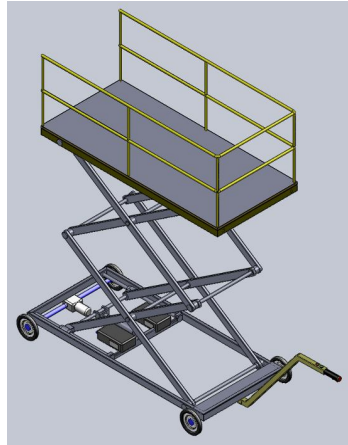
Vista isométrica do projeto CAD de FACEAR01.
